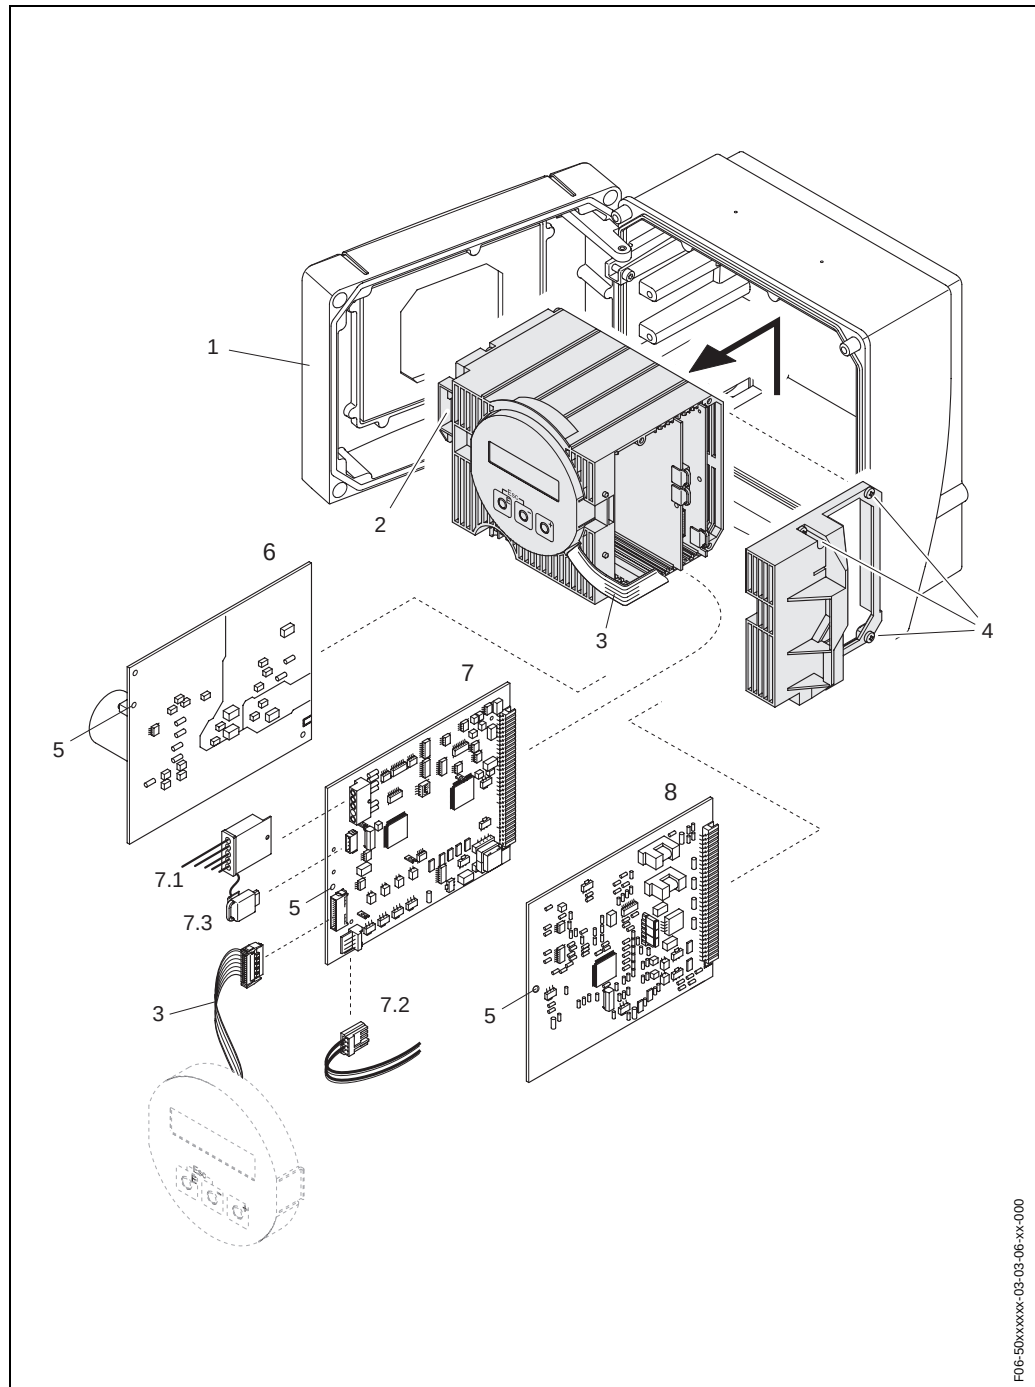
Alojamento com montagem de parede : removendo e instalando placas de circuito impresso
